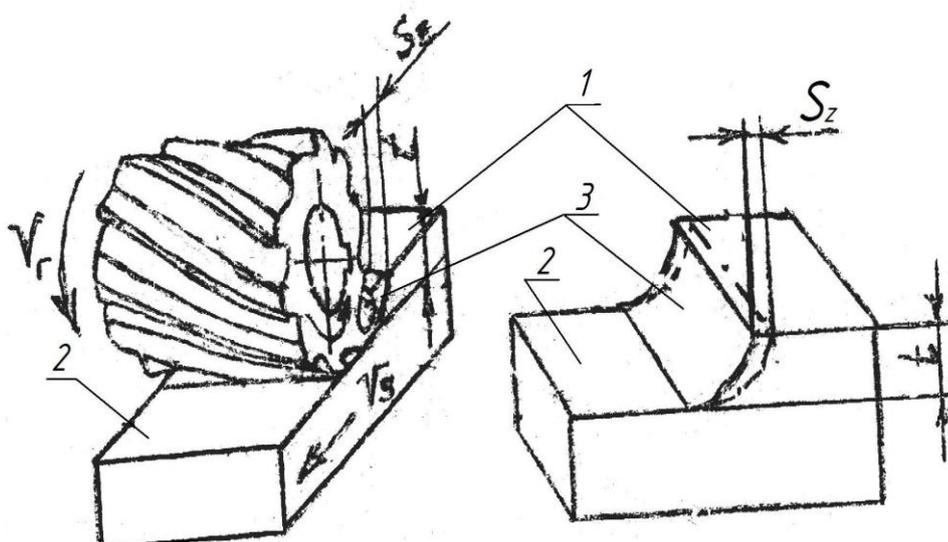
Поверхности заготовки при фрезеровании и элементы режимов резания
